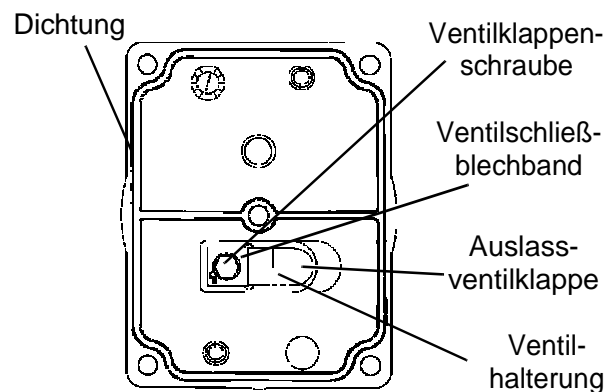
Kompressor und Kompressorkopf entfernen – Zusammenbau des Kompressors-Auslassventilklappe, Ventilhalterung und Ventilschließblechband
